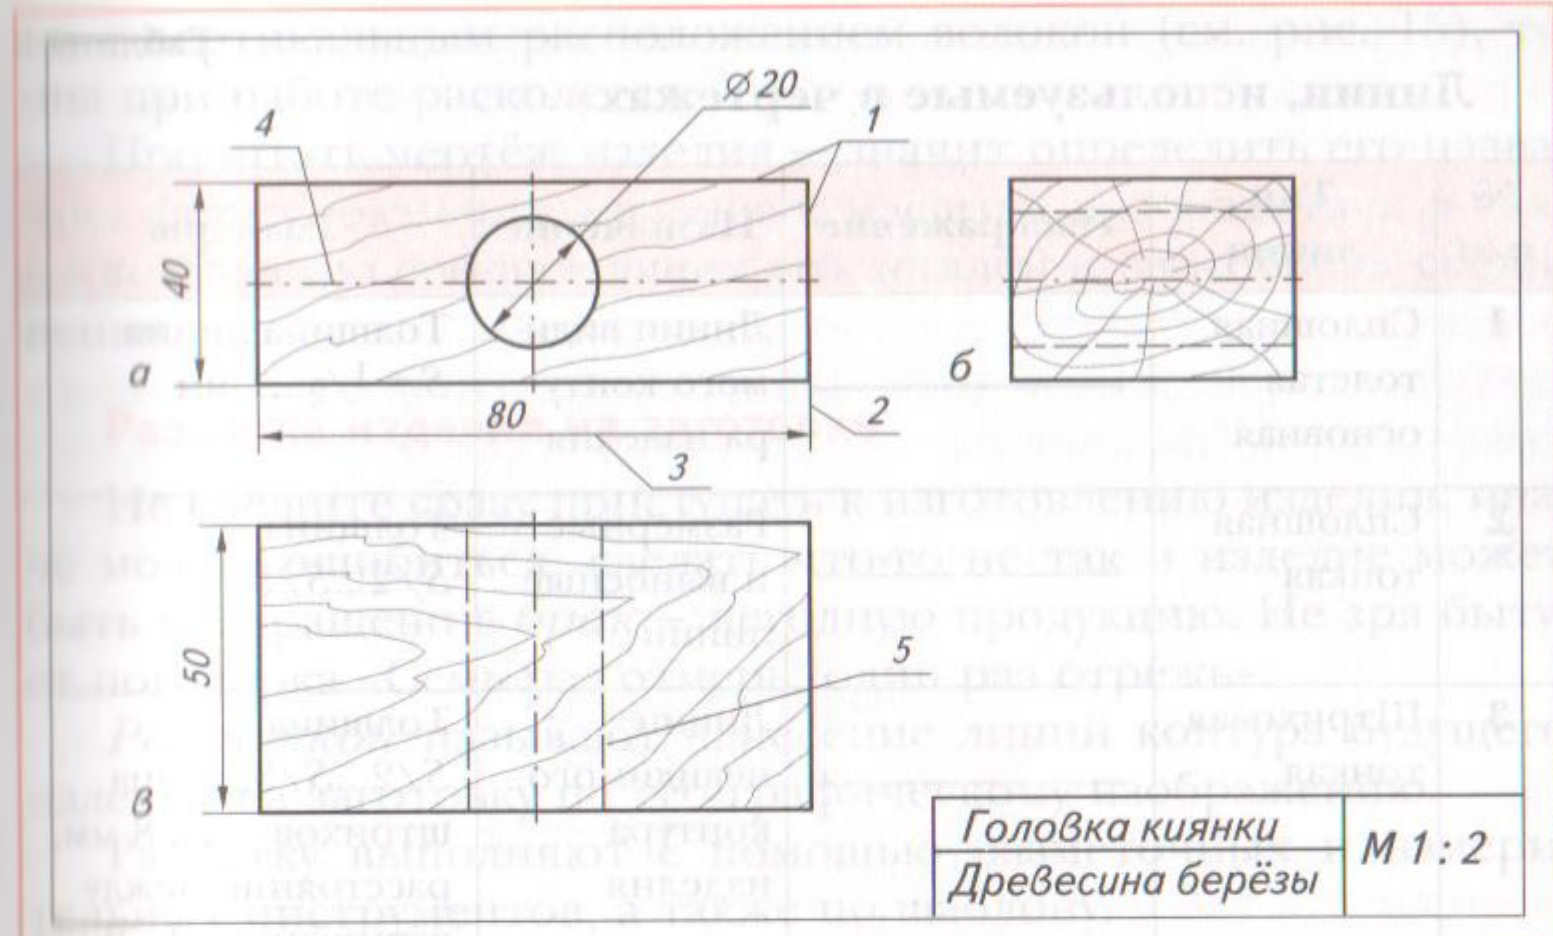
Чертёж детали: *a* — главный вид; *б* — вид слева; *в* — вид сверху. Линии изображения: 1 — линия контура детали (сплошная основная); 2 — выносная (сплошная тонкая); 3 — размерная (сплошная тонкая); 4 — осевая или линия симметрии (штрихпунктирная); 5 — невидимого контура отверстия (штриховая)
